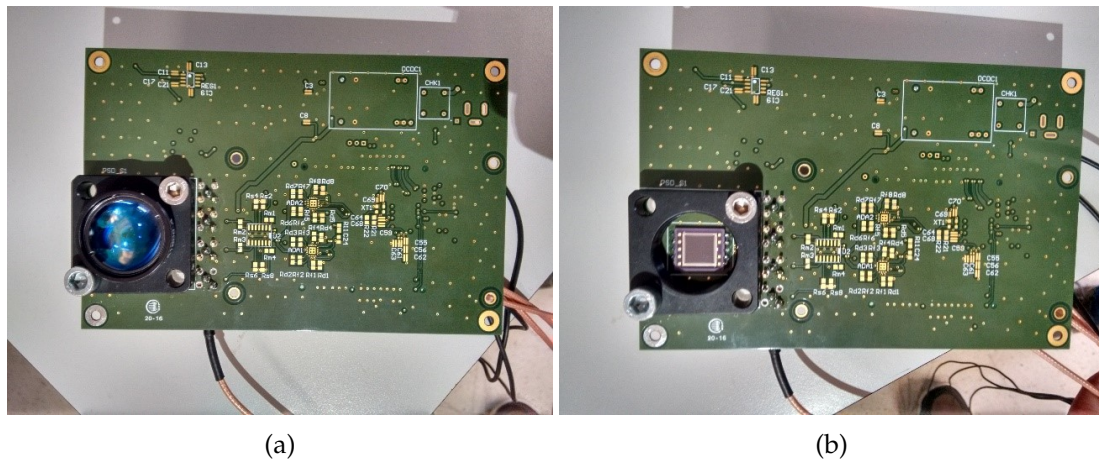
Placa de circuito impreso para sensor PSD; (a) PCB con lente; (b) PCB sin lente
